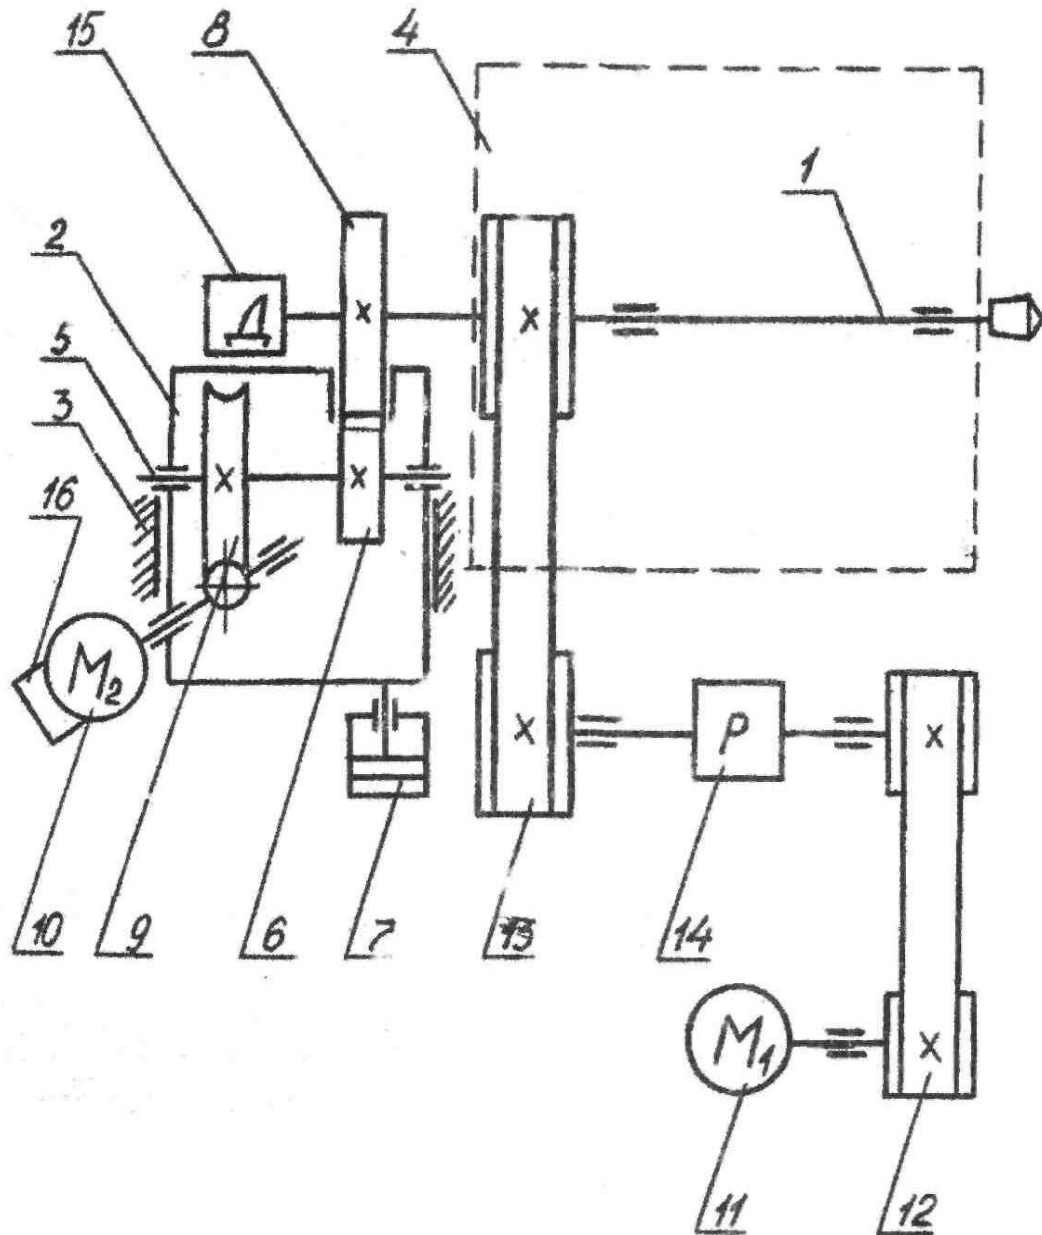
Кінематична схема приводу позиціювання шпинделя, виконана у вигляді автономного вузла з черв'ячним редуктором
